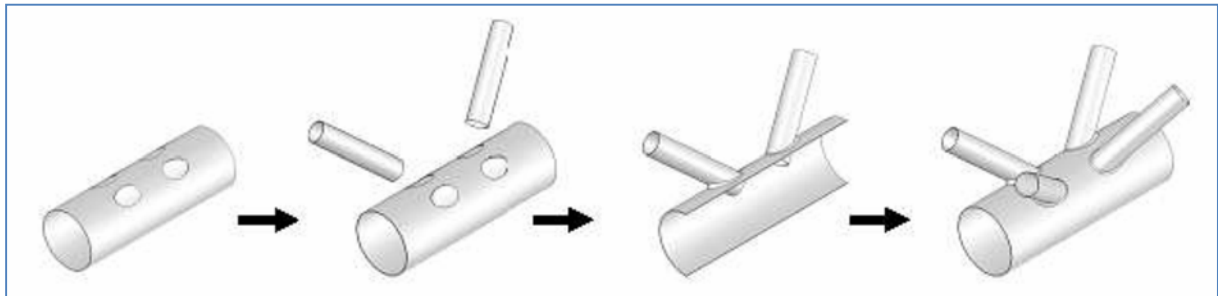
Soudage d'éléments tubulaires
